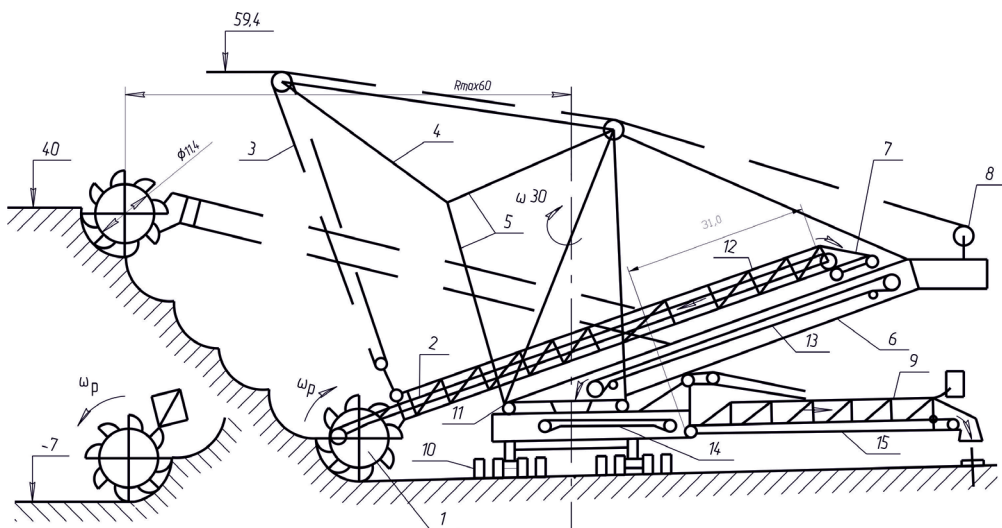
Конструктивная схема роторного экскаватора с выдвижной стрелой:
